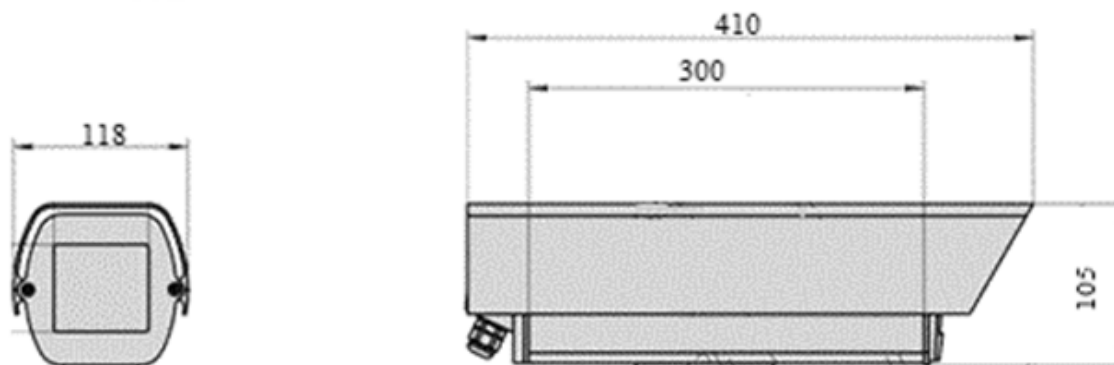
Габаритный чертеж видеокамеры ИВМС-701.
